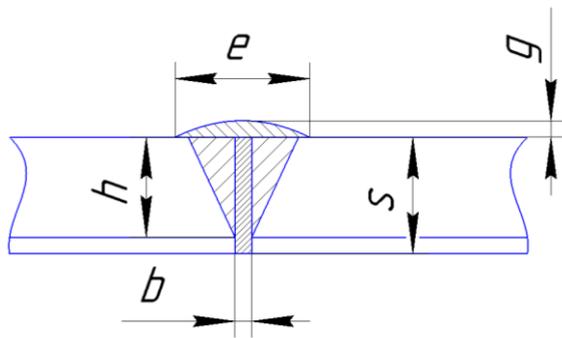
Размеры и номинальные значения сварного шва
